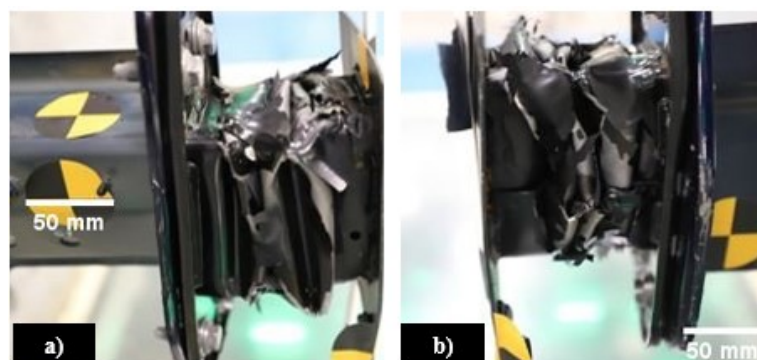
Pós teste: a) vista do lado esquerdo e b) vista do lado direito - Peça N°3
